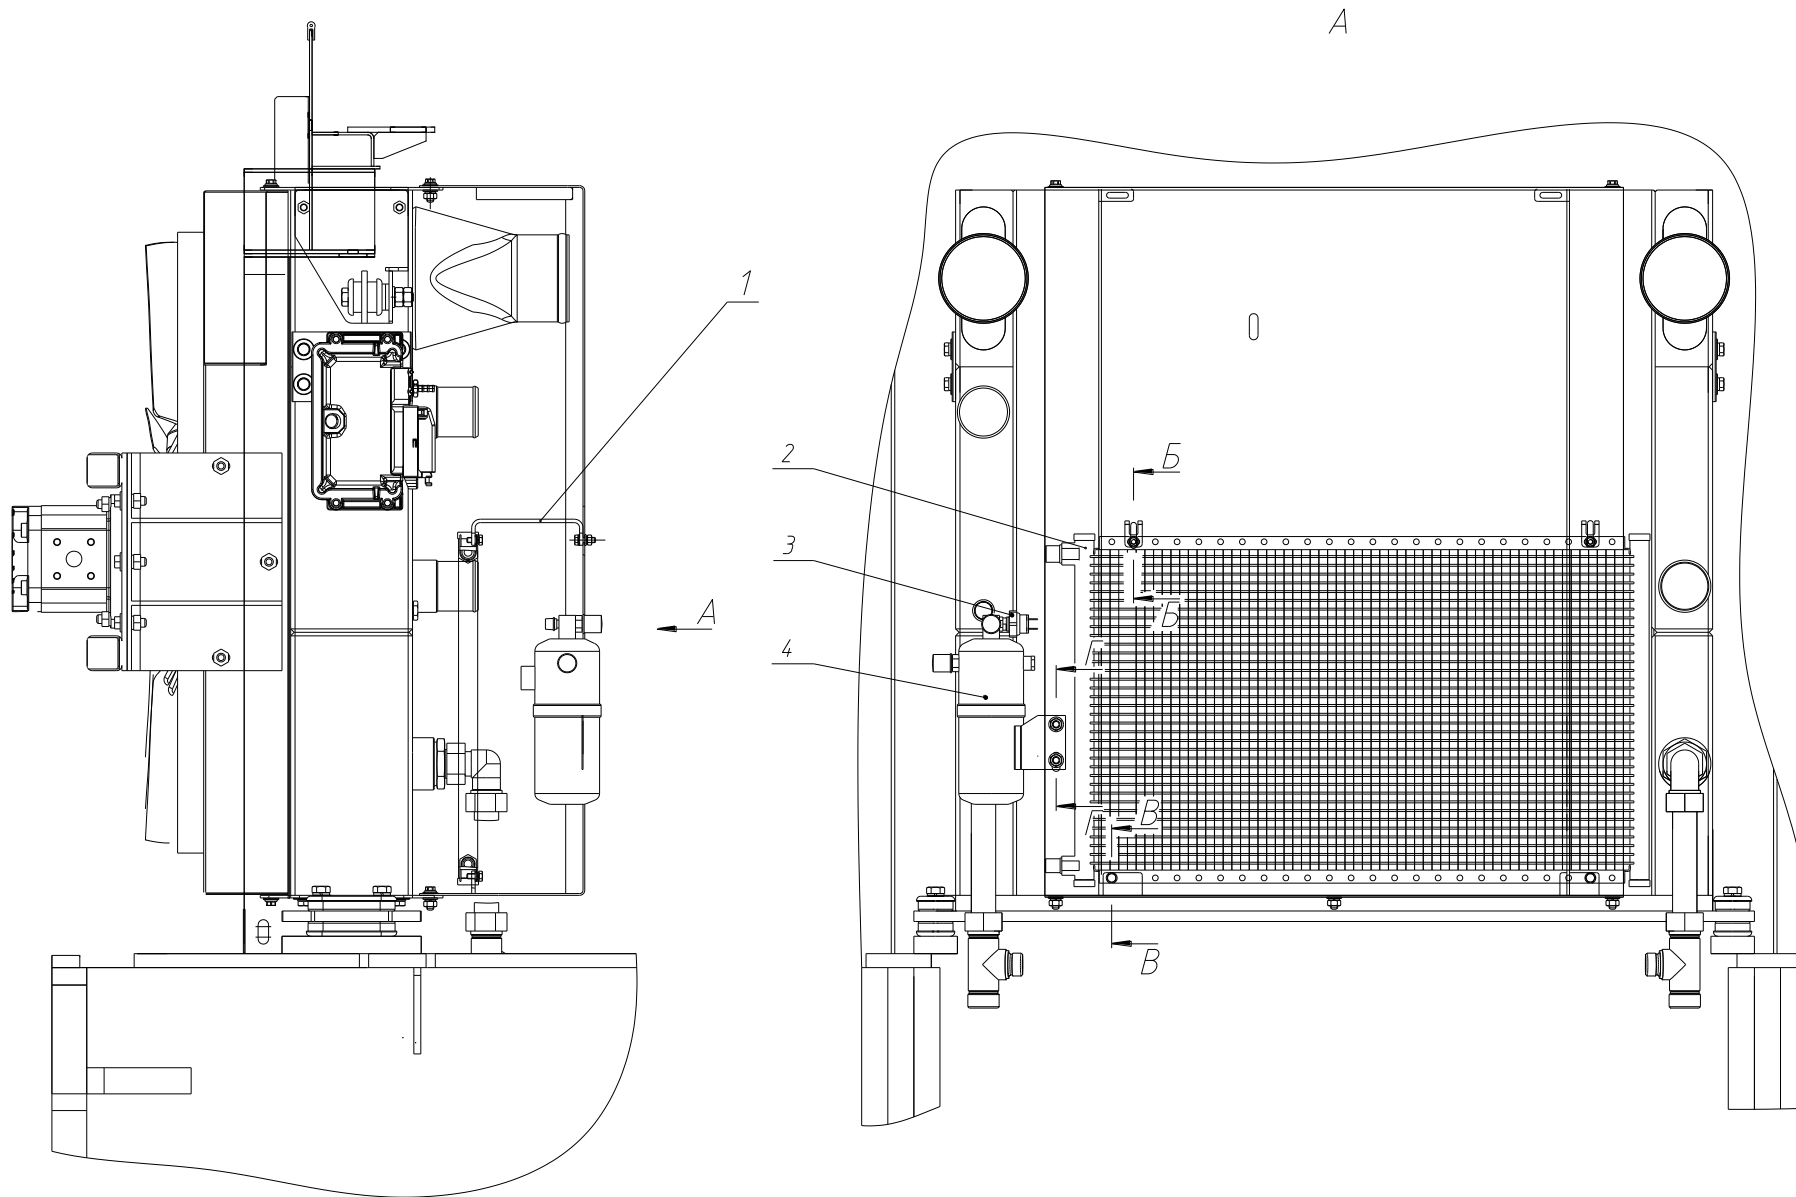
Установка конденсатора 760.31.03.00.000-01
